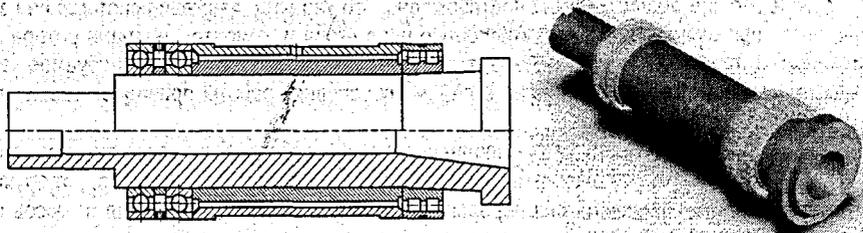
Эскизная компоновка и графическая 3D-модель шпиндельного узла станка ОРША Ф32Ш
